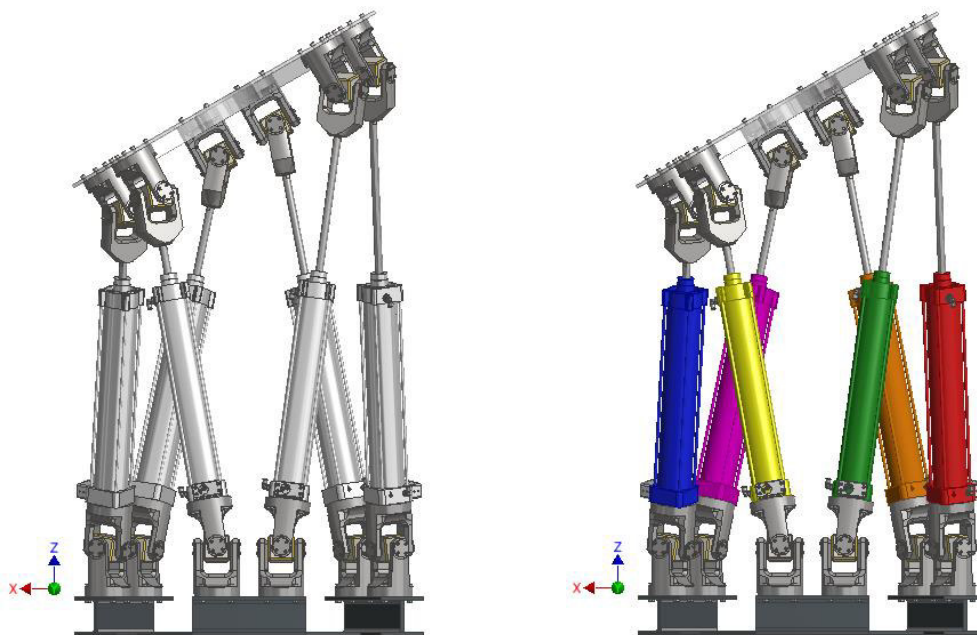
Giro en el eje Y de la plataforma Stewart-Gough (Vista de plano YZ)
